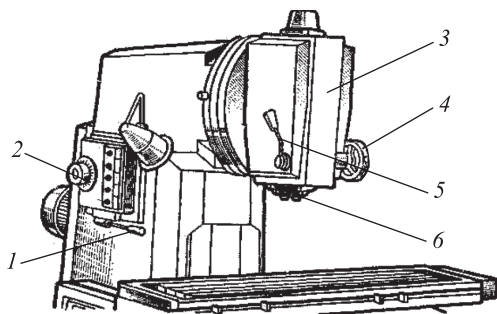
Конструктивные особенности вертикального консольно-фрезерного станка модели 6P12
